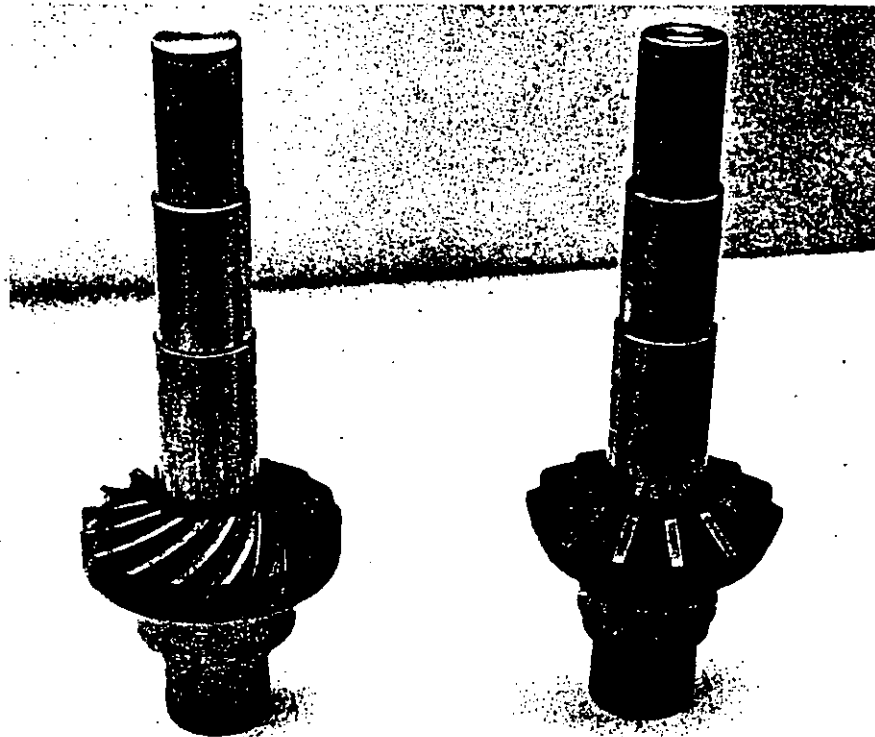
Engranés del reductor; original a la derecha, optimado a la izquierda.
